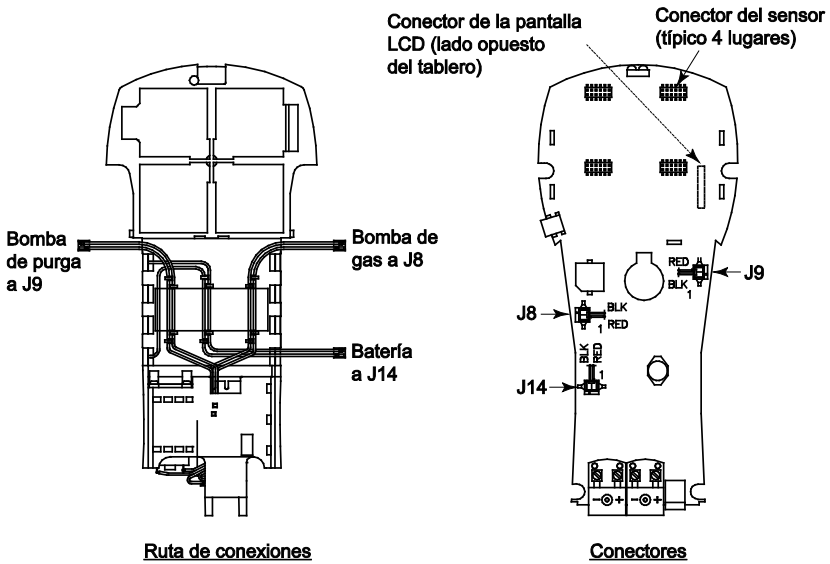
Ruta de conexiones, conectores y soldadura
